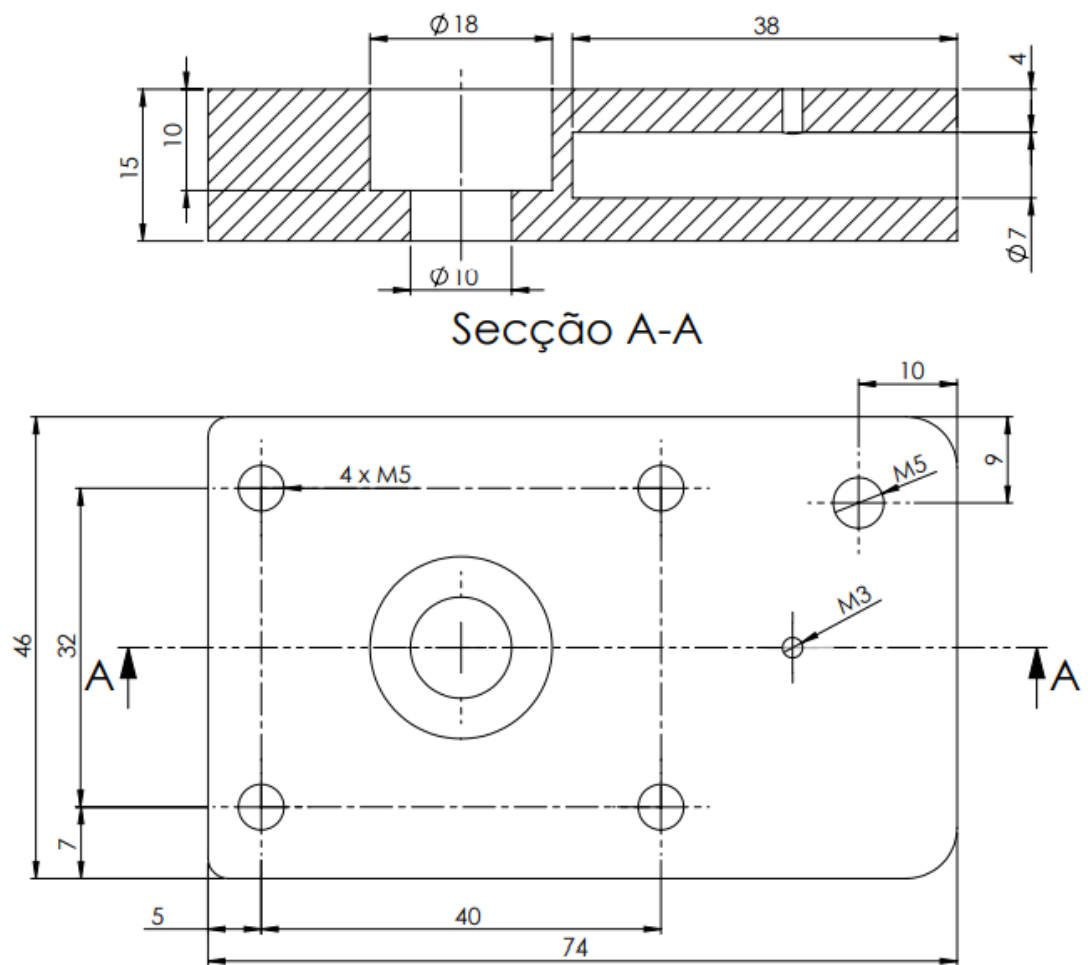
Desenho técnico da Base do *Shoulder*.
